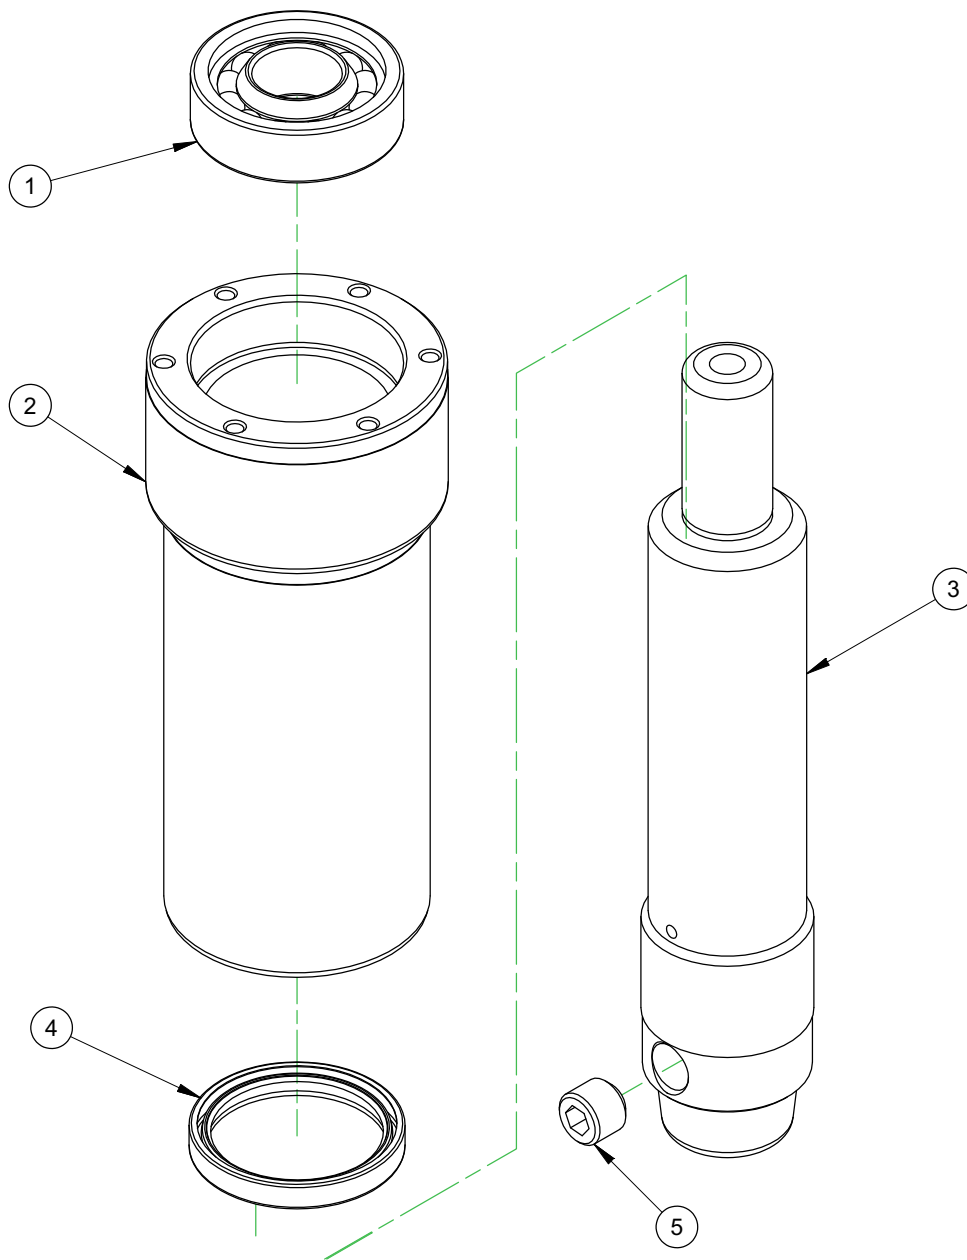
CONJUNTO DE CAJA DE ENGRANAJES DE 3,5 RELACIONES (N/P 103341)
